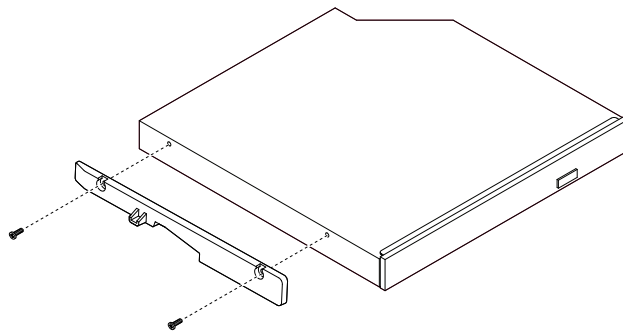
Halterung für flaches optisches Laufwerk installieren
